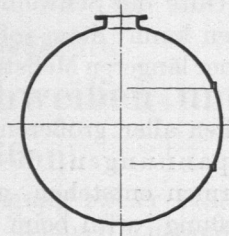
Geschweißtes kugeliges Gefäß.
